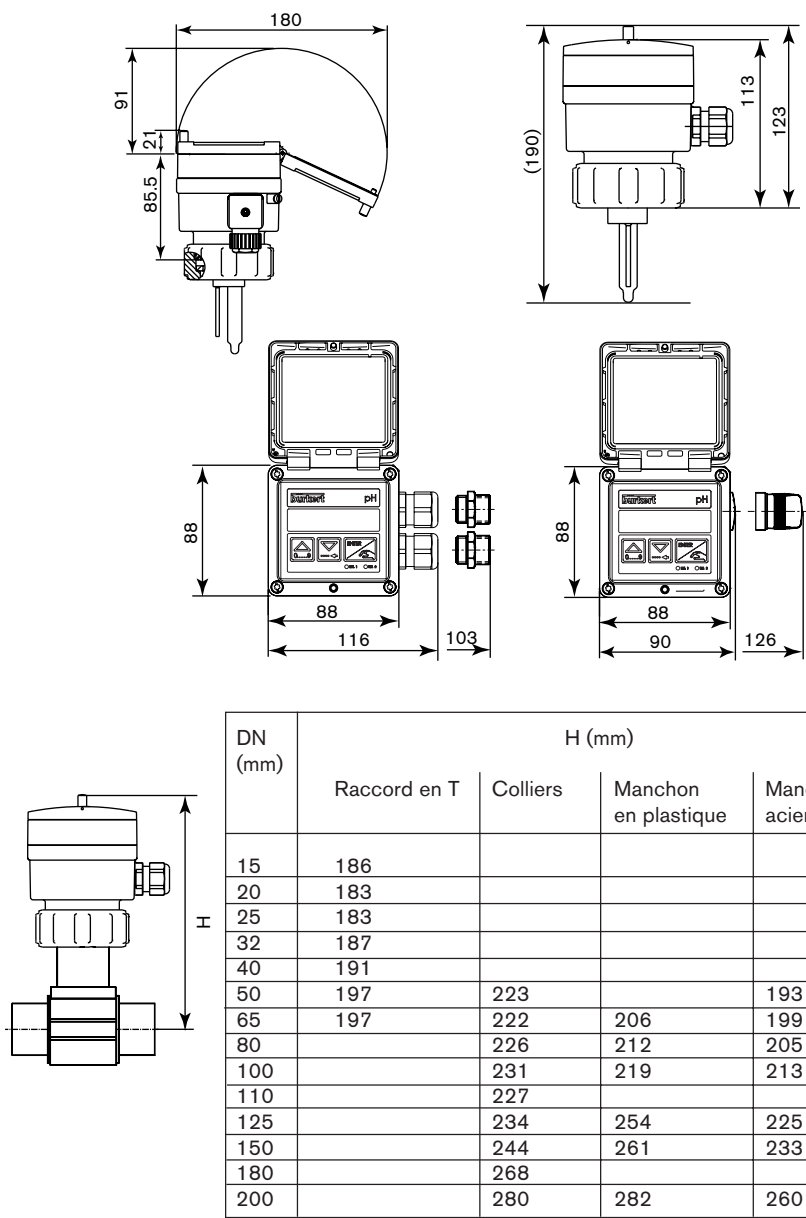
Dimensions du régulateur de pH 8205 compact
